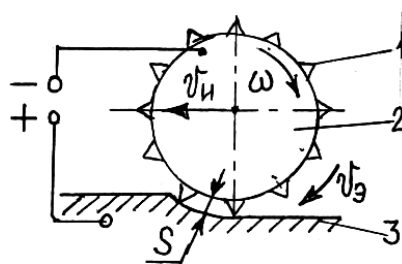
Схема анодно-абразивного шліфування: 1 – абразивне зерно; 2 – інструмент (круг); 3 – заготовка
